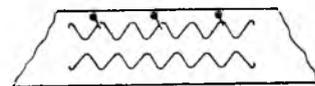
Фиксирование гвоздями на доске или стене сарая растянутой по шаблону спирали проволоки
